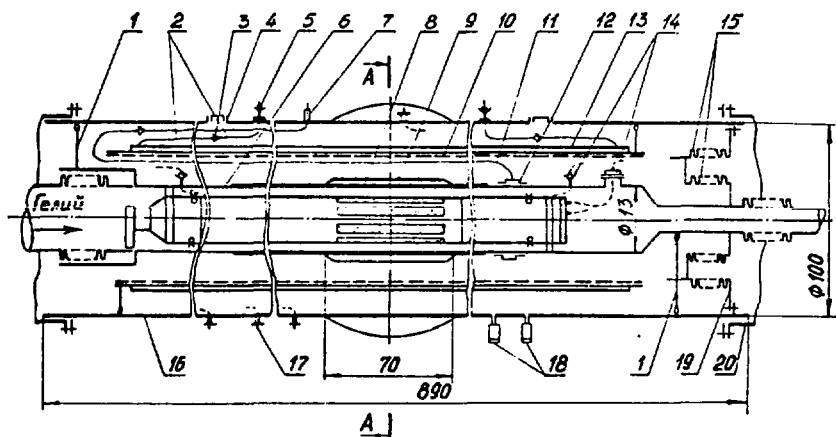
Схематичная конструкция проточного криостата для СТВЭ. 1 — центрирующая вставка; 2 — азотные трубки; 3 — разъемное соединение; 4 — люк; 5 — герметичный узел с тепловой развязкой; 6 — гелиевый канал; 7 — узел вывода импульсной трубки; 8 — труба из молибденового стекла; 9 — окно; 10 — промежуточный экран; 11 — импульсная трубка; 12 — камера отбора давления; 13 — азотный экран; 14, 17 — герметичные разъемы на гелиевом канале и вакуумном корпусе соответственно; 15 — тепловой мост; 16 — вакуумный корпус; 18 — средства измерения вакуума; 19 — узел уплотнения; 20 — вакуумная муфта. (Сечение А-А см. на рис.7).
